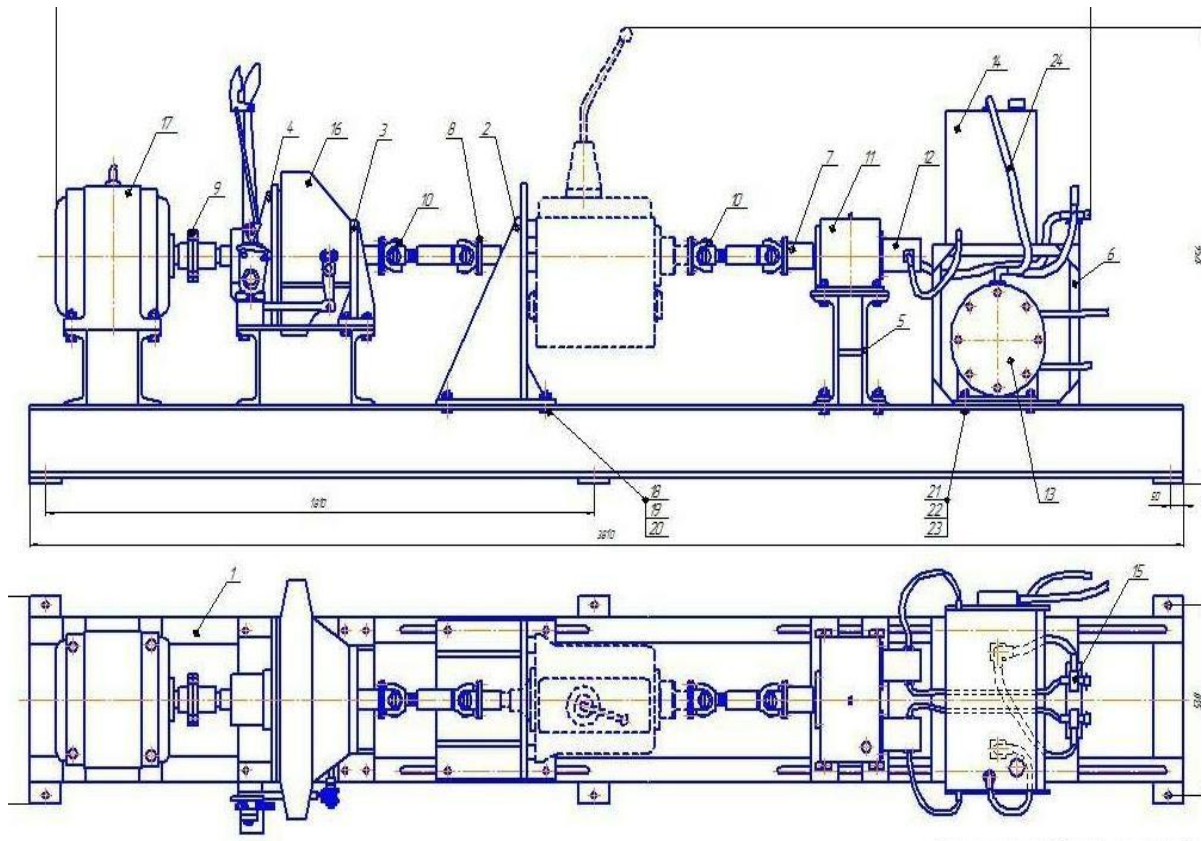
Універсальний стенд для обкатки коробок передач.
